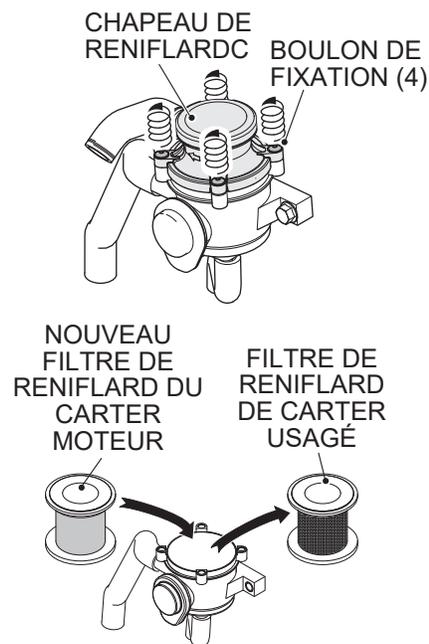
Remplacement du filtre d'aération du carter de vilebrequin
